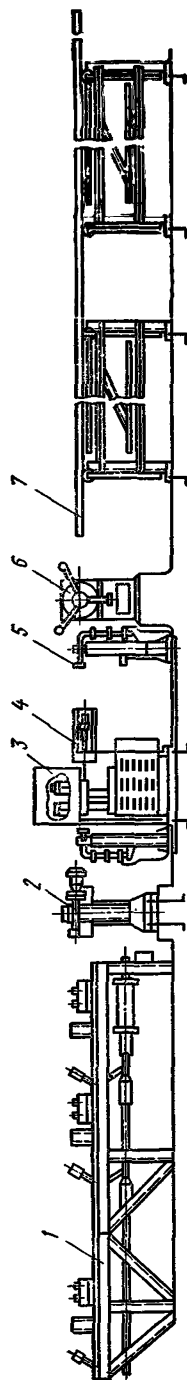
Схема установки СМЖ-32 для сварки плетей стержневой арматуры и высадки анкерных головок: 1, 7 — приемный и подающий конвейеры, 2 — механизм подачи, 3 — машина для стыковой сварки, 4 — воздуховодораспределитель, 5 — стойка с подвешенным роликом, 6 — станок для резки
